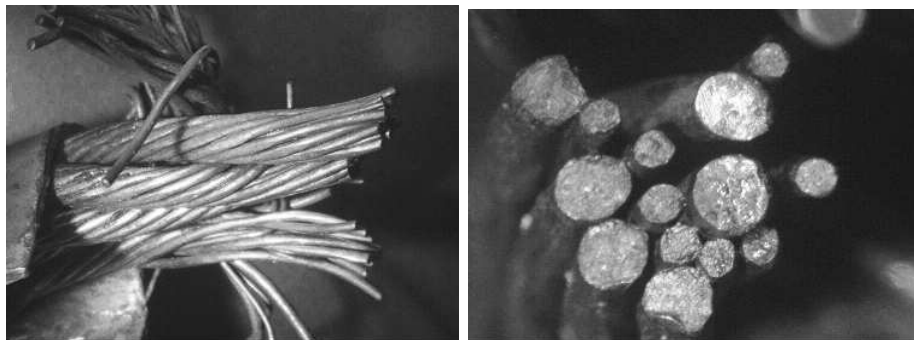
Cable 1 (izquierda). Cable 2 (derecha).  $0,2x$
